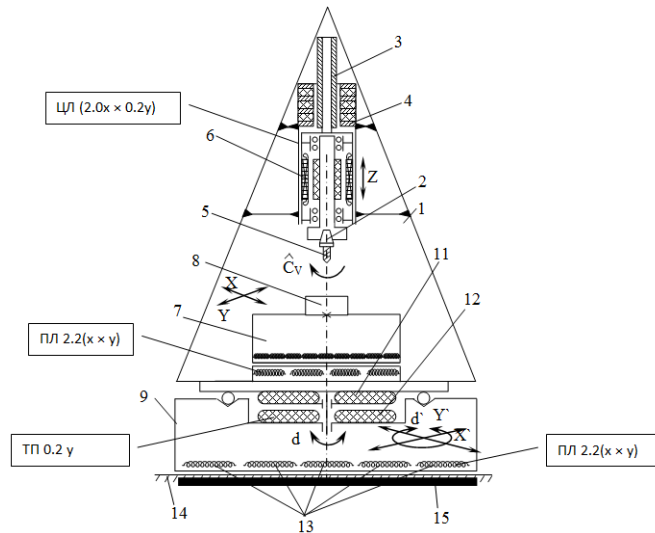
Багатокоординатний мобільний свердильно-фрезерний верстат-робот без механічних передач с генетичними формулами
